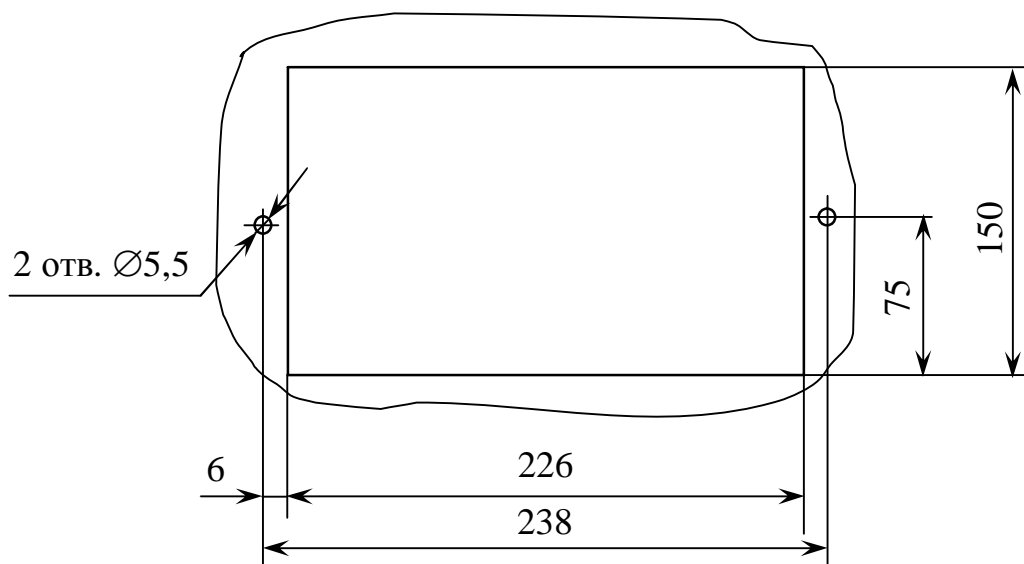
Расположение отверстий для крепления блока преобразовательного щитового исполнения
